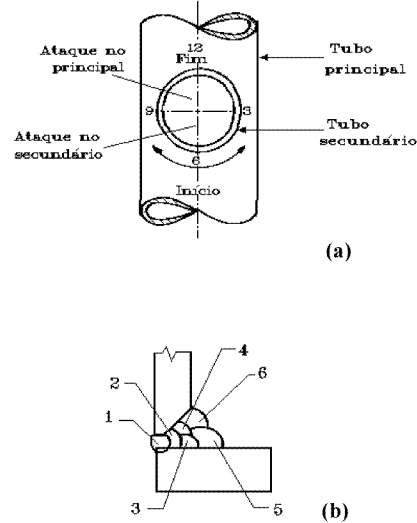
Soldagem de conexão de tubo com chanfro de 45° no secundário: (a) Progressão da solda; (b) Seqüência de deposição dos passes.
